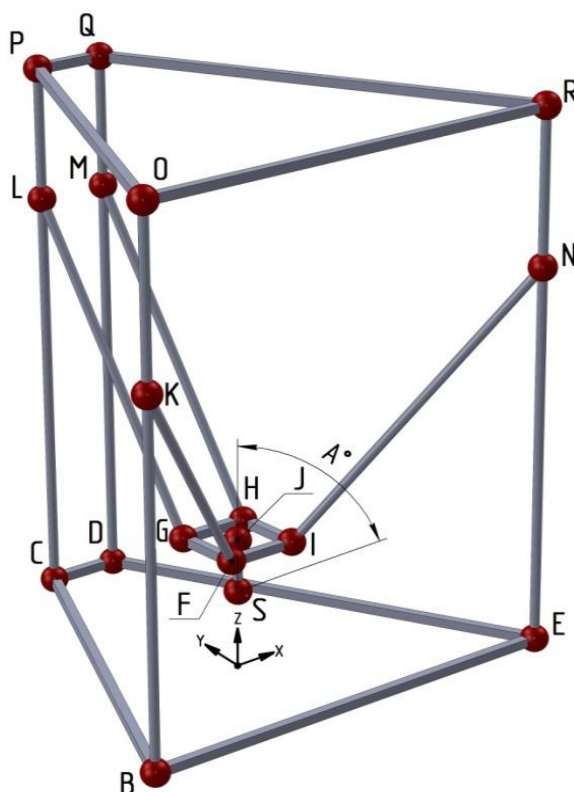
Structural 3D-model of multiaxis milling machines with PKM / Структурна 3D-модель багатокординатного фрезерного верстату з МПС
